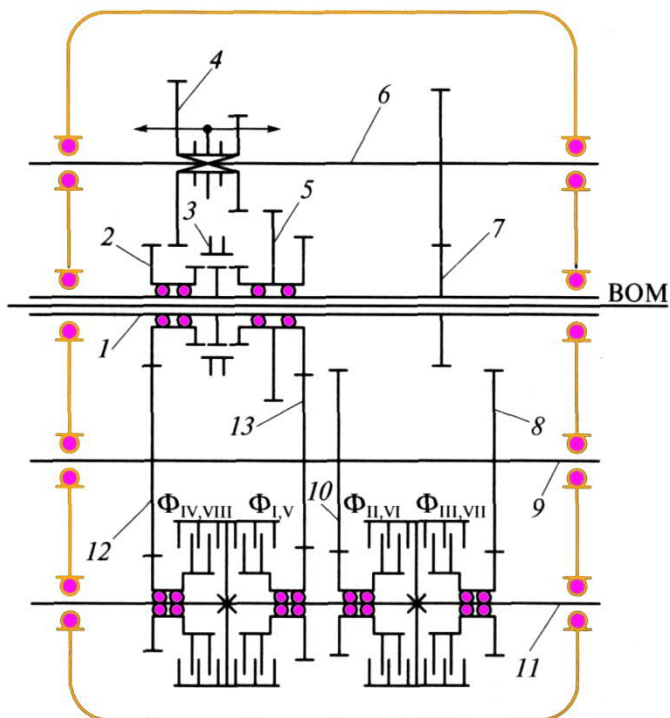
Кинематическая схема коробки передач с фрикционным включением:
